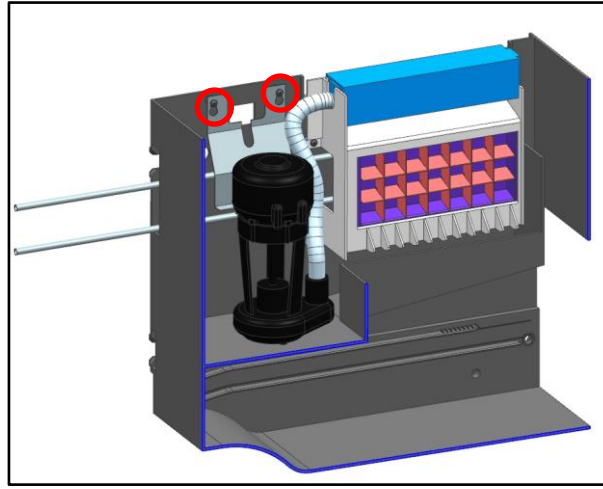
Buz kabı şasisinin, buz makinası şasisine montajı-2.
